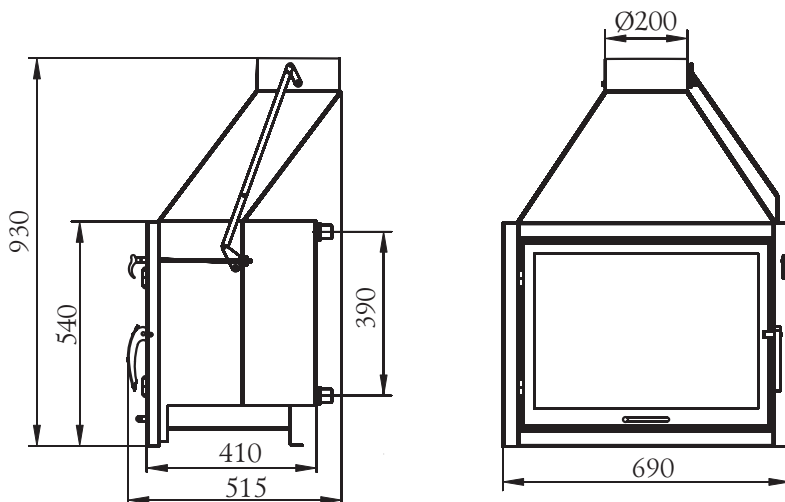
Габаритные размеры каминной топки «Аквариус ТО».
